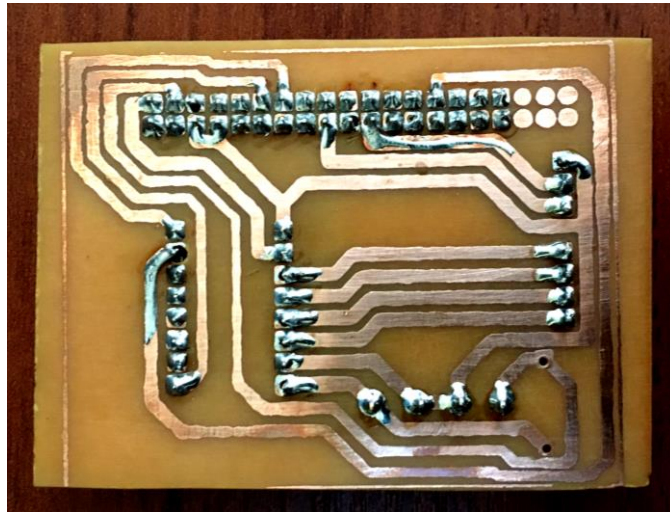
16: Perforación y soldadura de las pistas electrónicas.
